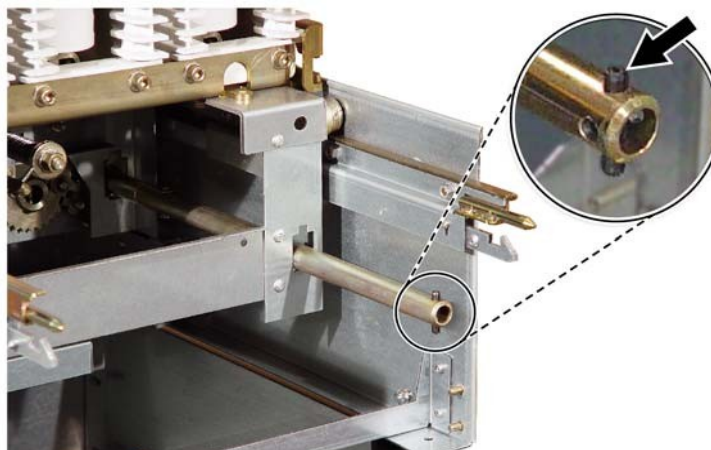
Соединительный штифт на валу управления заземляющего ножа
